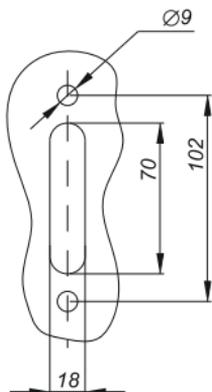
Размеры отверстий в оболочке для установки привода передней смещенной рукоятки
